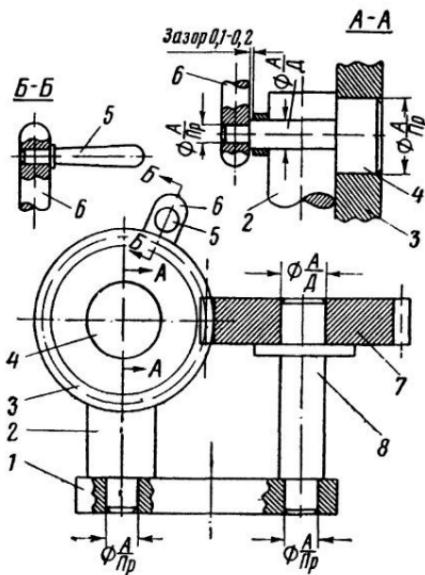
Модель передачи с винтовыми зубчатыми колесами (схема соединения деталей).
